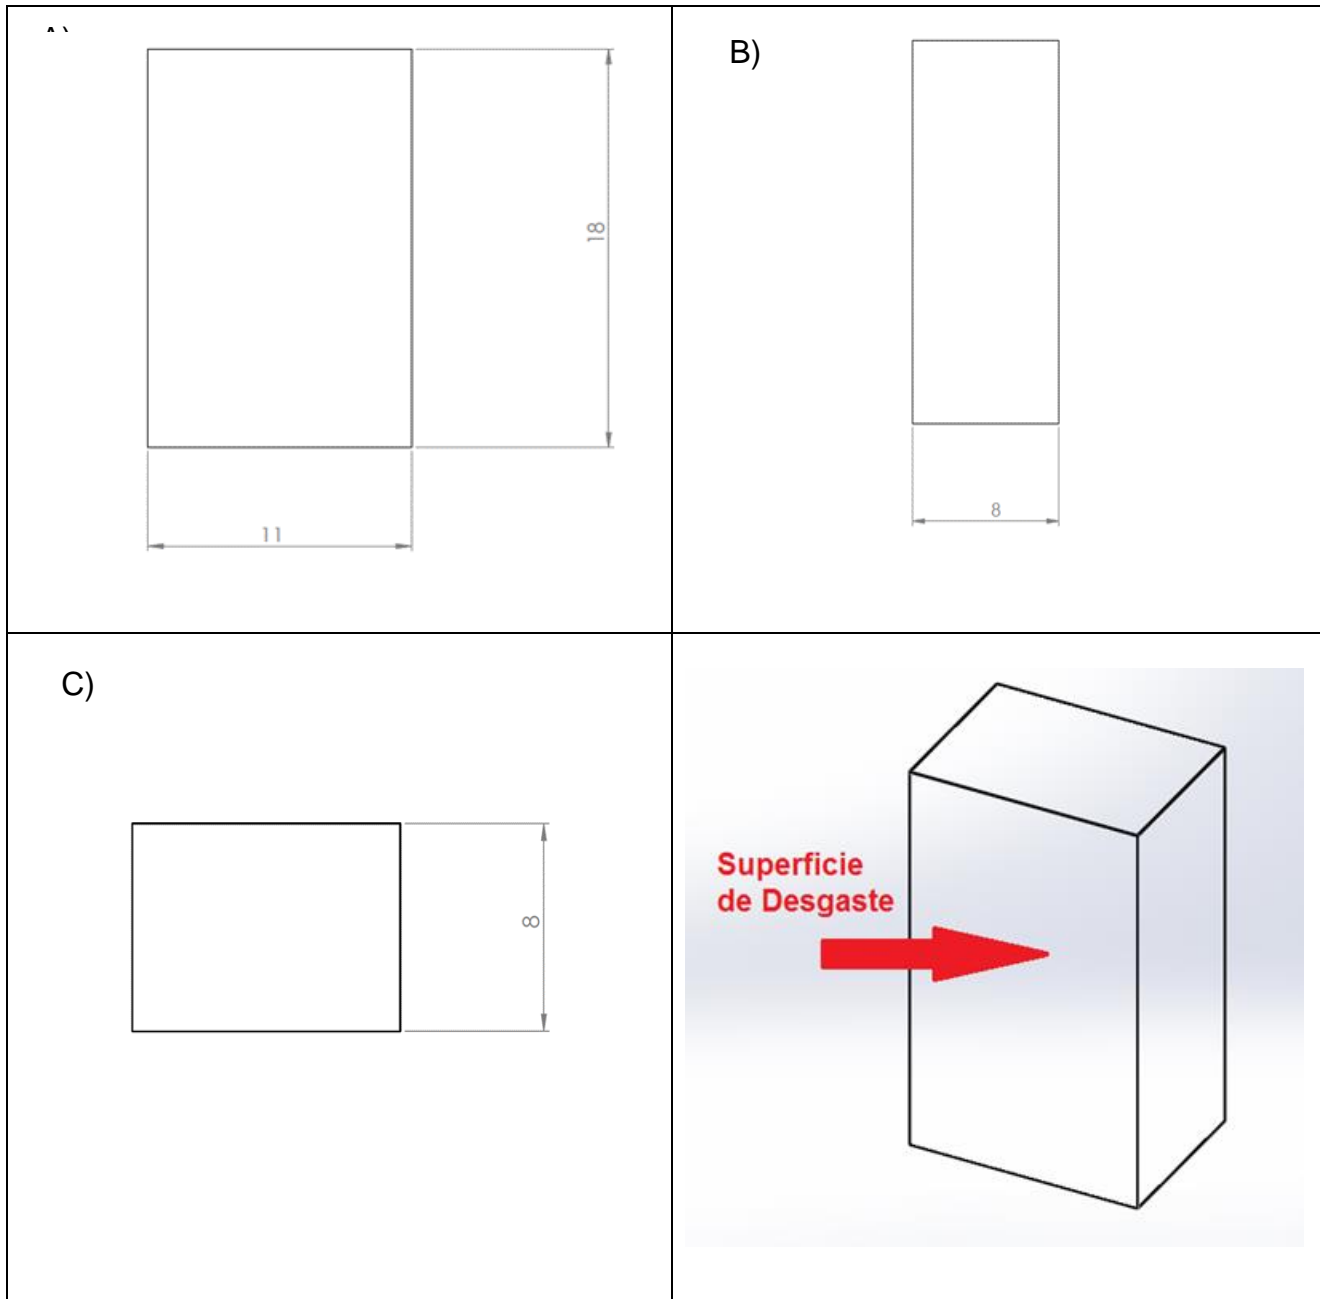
Esquema de muestras para ensayo de desgaste abrasivo. A) Vista frontal. B) Vista lateral. C) Vista Inferior. D) Esquema 3D de muestra. (Dimensiones en mm)
